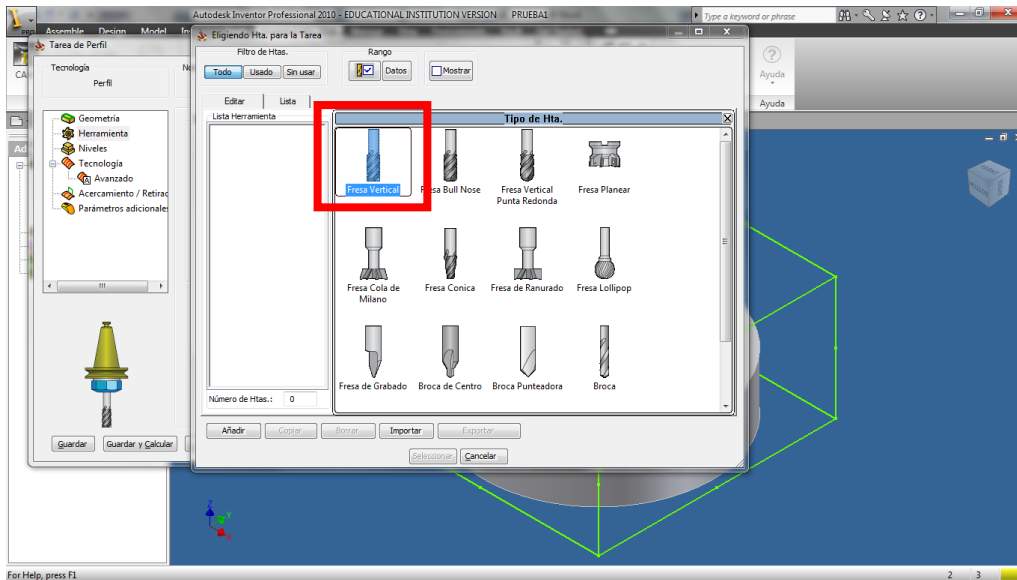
Maquinado Fresadora CNC – Selección de tipo de fresa
